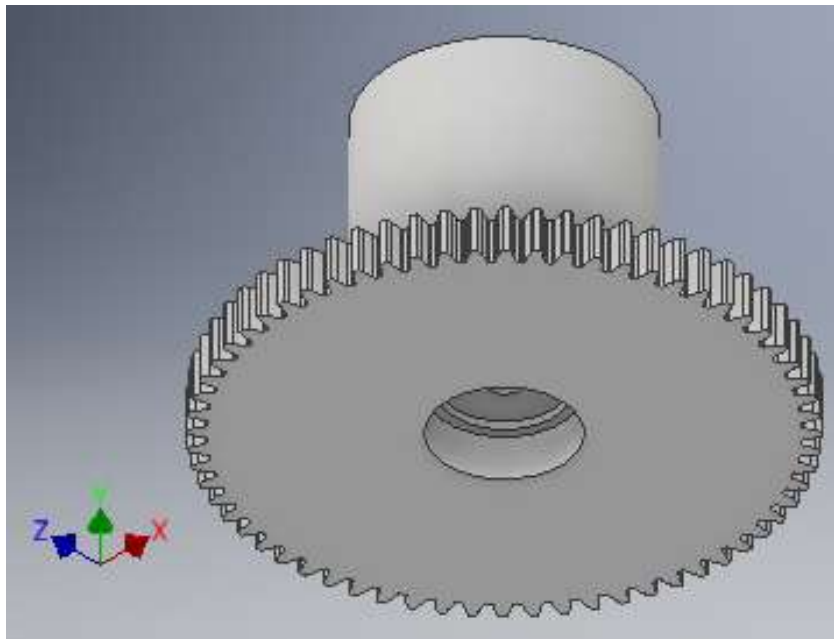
Vista inferior de la pieza de enlace mecánico.
